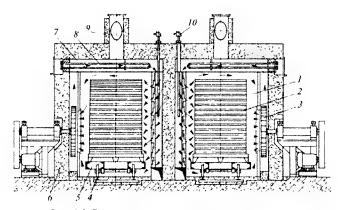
Бакели затор (вулканн затор) двухкамерный: I =камера; 2 =теплоноентель (горячии воздух); 3 =вентилятор; 4 =рельсовый нут; 5 =этажерка; 6 =шлаковата; 7 =электрический калорифер; 8 =трубчатые электронагреватели; 9 =трубчатые вытяжной вентиляции, 10 =термоэлектрические преобразователи
